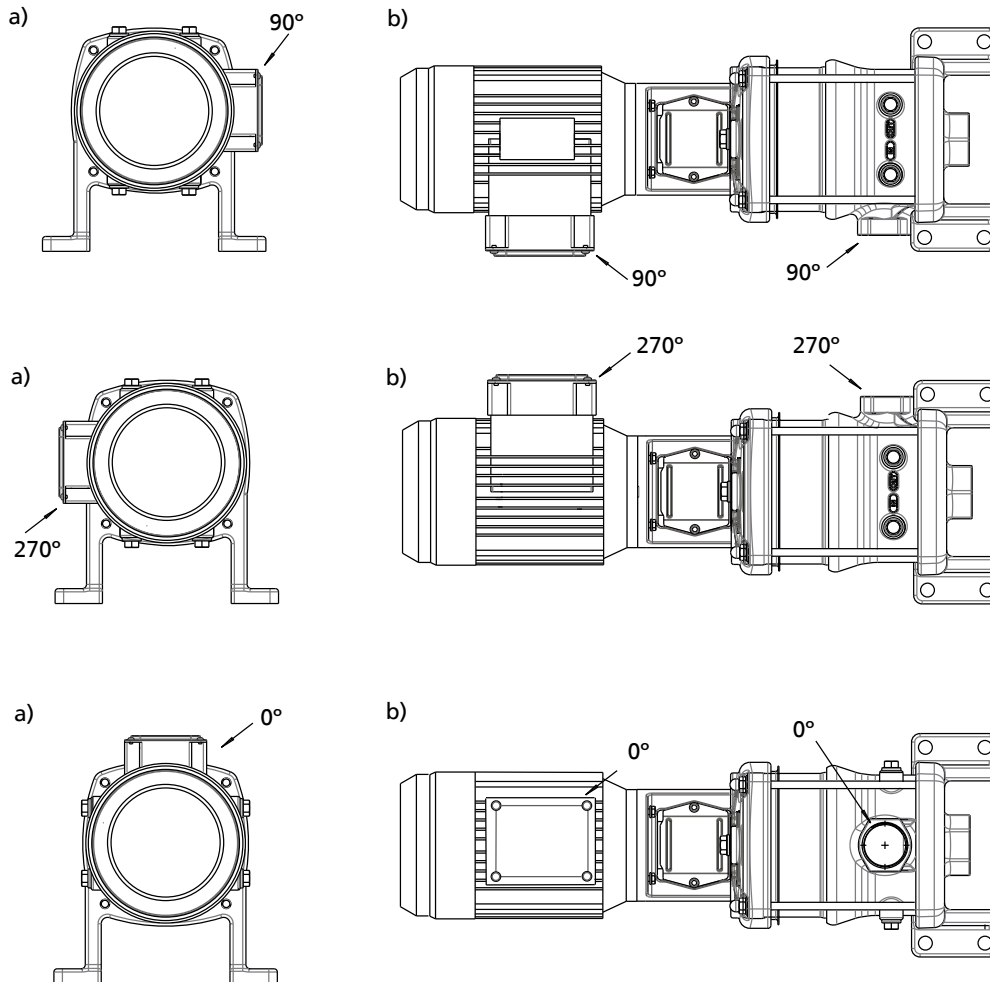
Optionale Aufstellungsarten für Position Klemmenkasten = Position Anschluss Druckseite a) Seitenansicht (vom Motor aus gesehen) b) Draufsicht
